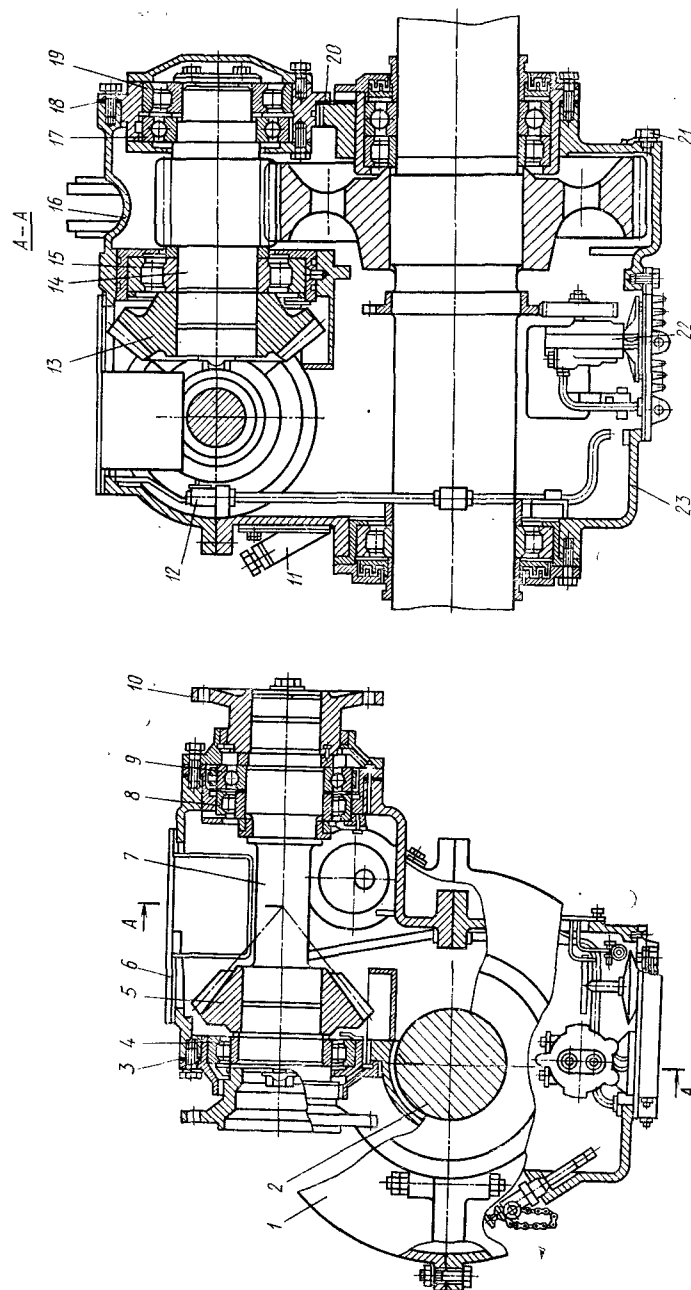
Двухступенчатый осевой редуктор тепловоза ТГМ4:
